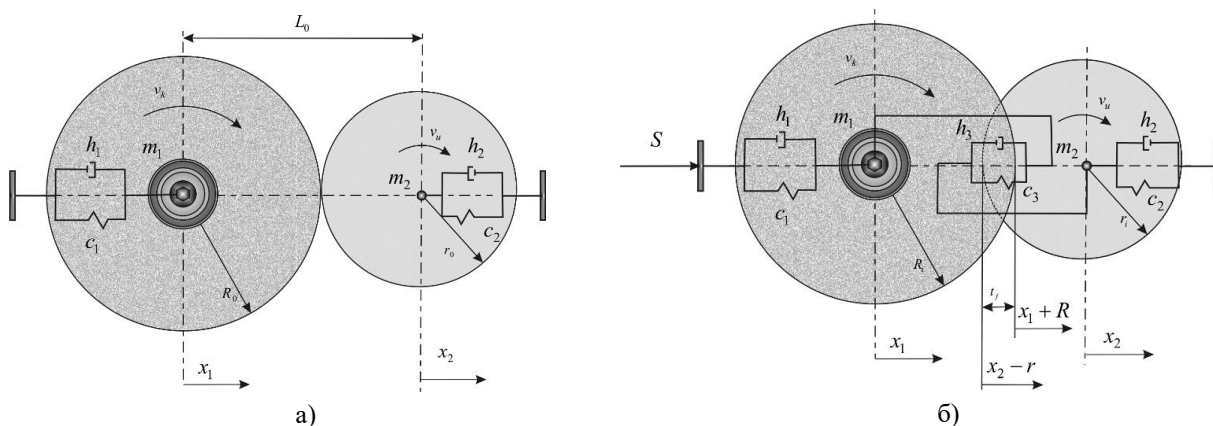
Эквивалентная схема динамической системы круглошлифовального станка
